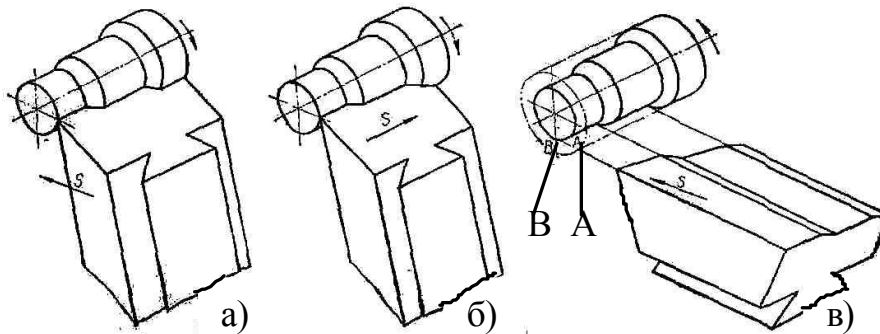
Схемы обработки поверхности вращения фасонными резцами
